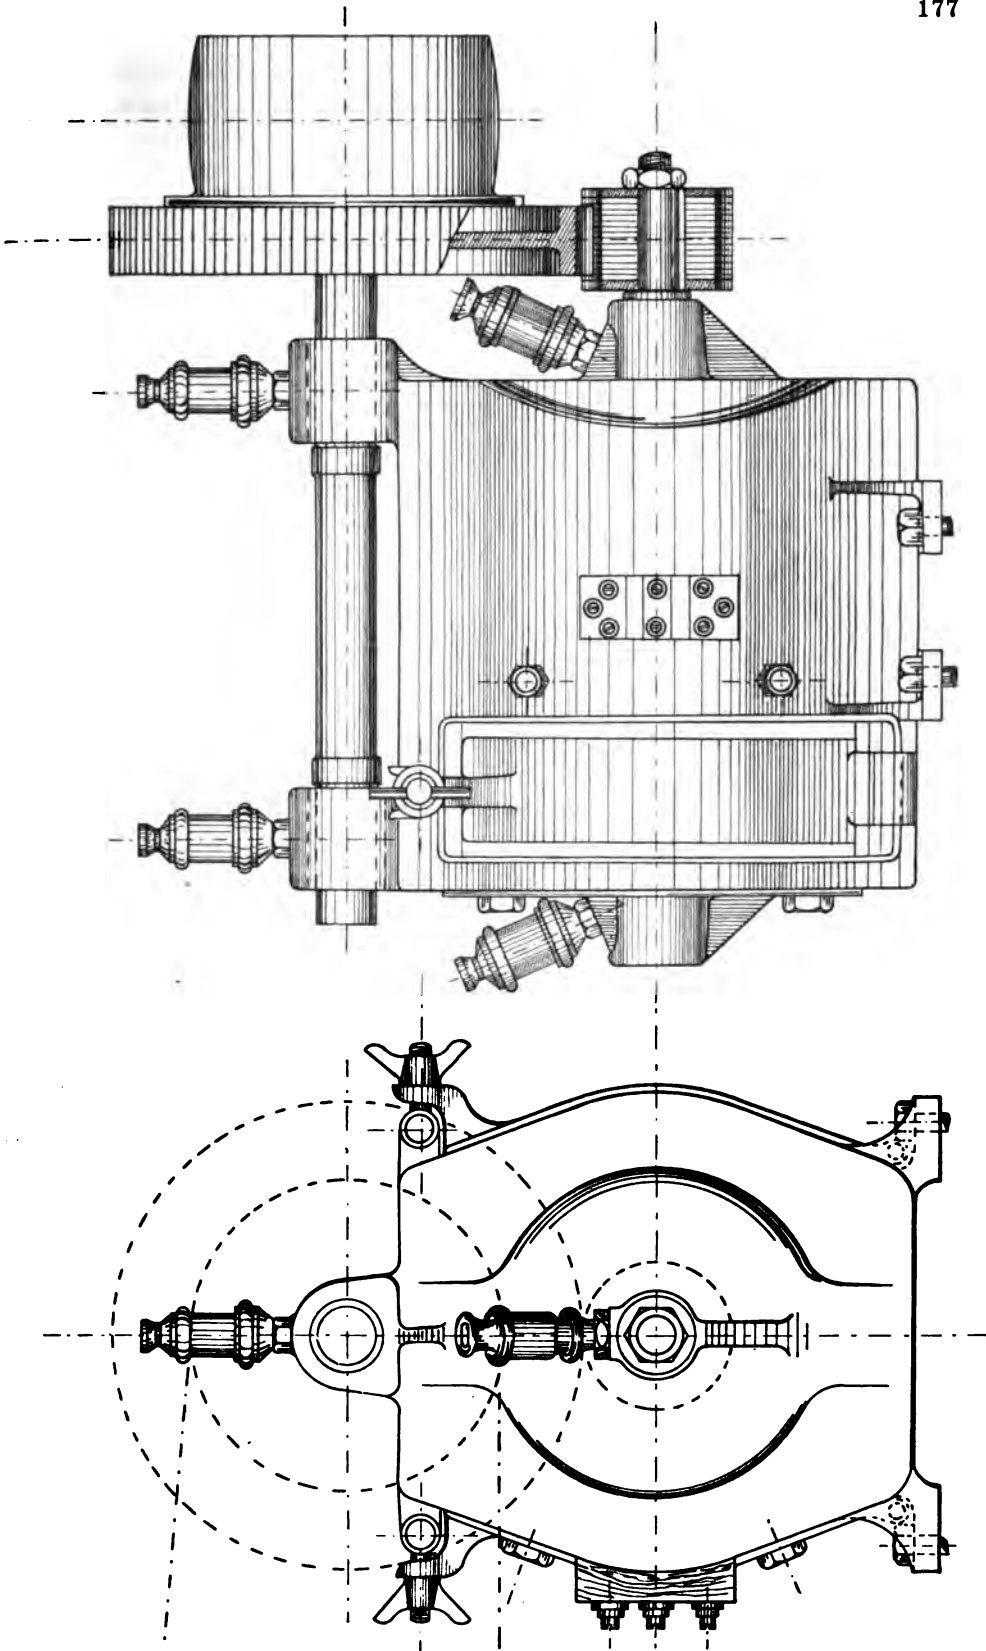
Kapselmotor mit Vorgelege der Magdeburger Elektromotorenfabrik.
